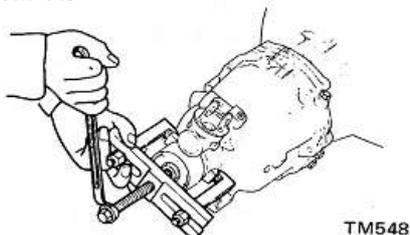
Dépose du jonc d'arrêt du roulement de l'arbre primaire
